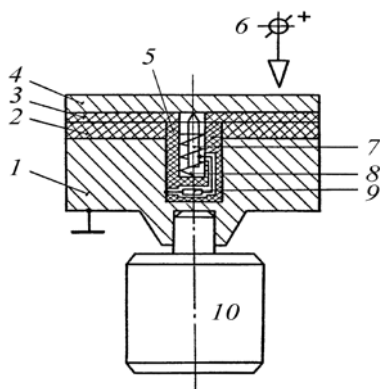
Схема центрифуги с электростатическим закреплением обрабатываемой пластины: 1 – металлический столик; 2 – полупроводящий слой; 3 – диэлектрический слой; 4 – закрепляемая пластина; 5 – изолирующий цилиндр; 6 – зарядный электрод; 7 – подвижный контактный электрод; 8 – пружинка; 9 – ограничительное сопротивление; 10 – электродвигатель вращения столика центрифуги
